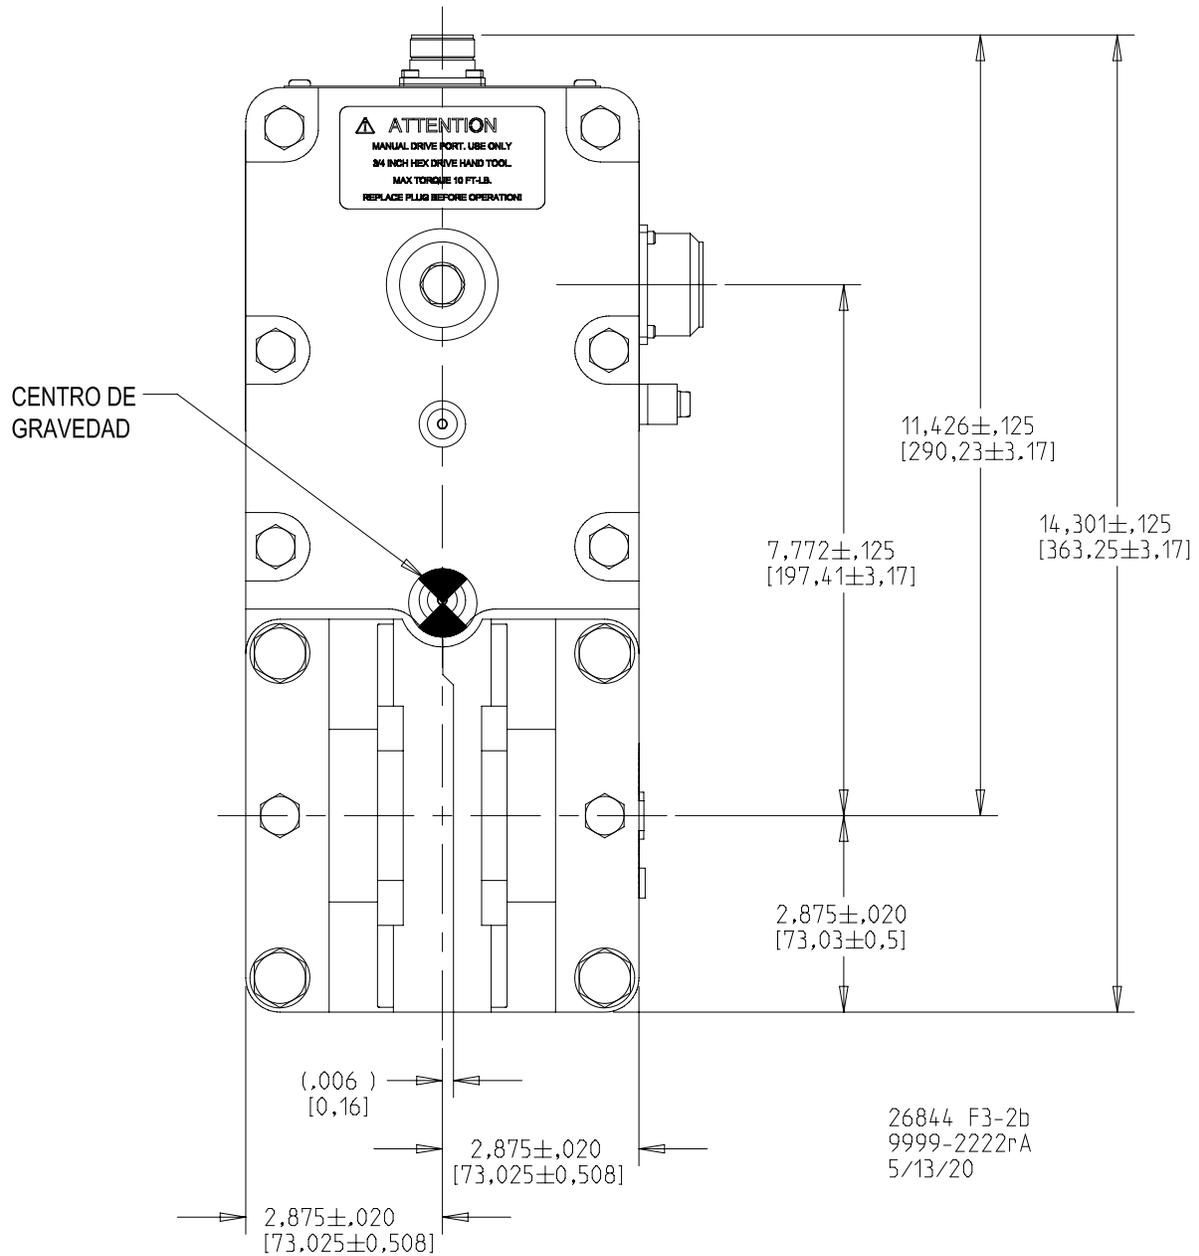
Dimensiones del ELA 80 (versión de horquilla giratoria)
